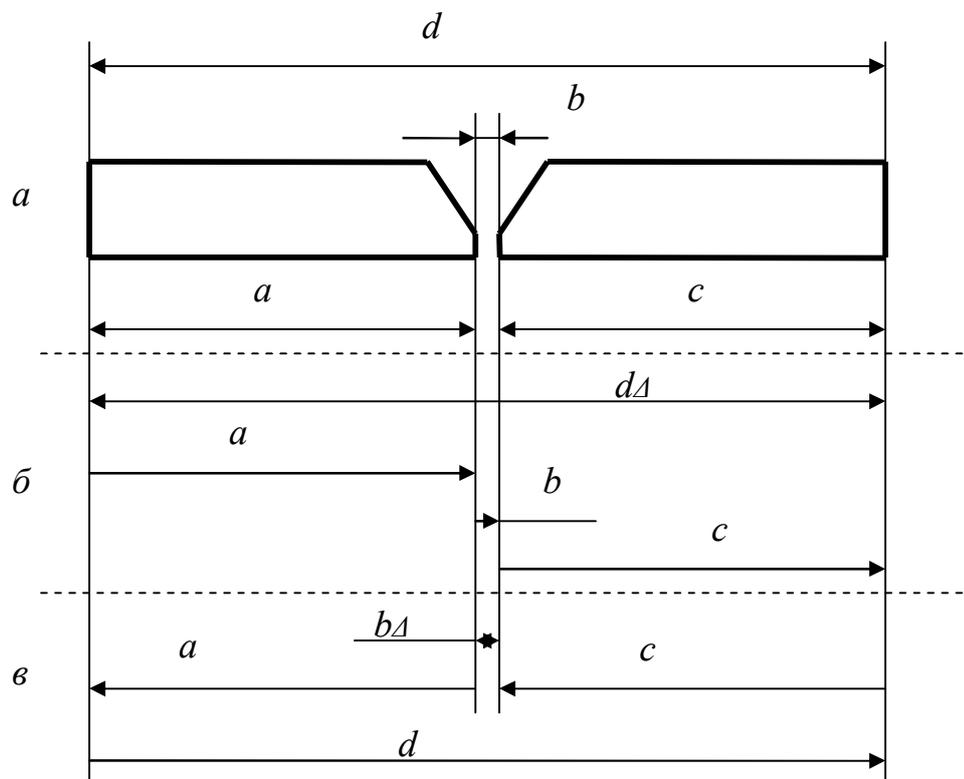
Сборочные размерные цепи в сварном изделии
